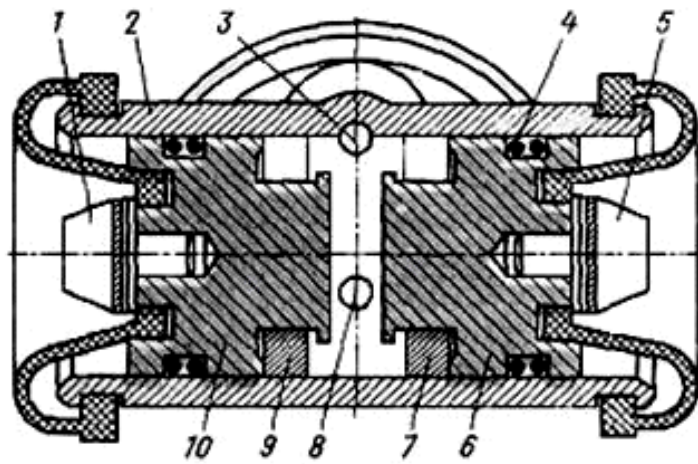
Колесный тормозной цилиндр автомобиля ГАЗ-24 "Волга"
